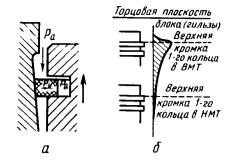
Износ зеркала цилиндра: а — примерная схема действия основных сил на поршневое кольцо при движении вверх; 6 — кривая износа цилиндра компрессора по образующей
